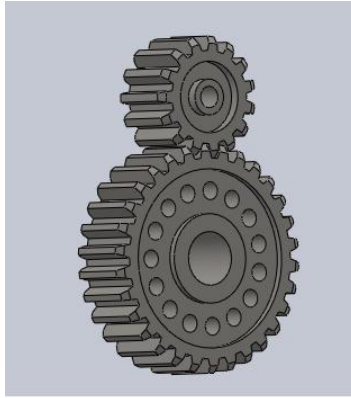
Sistema de engranajes para la transmisión de potencia del servomotor, el piñón se denomina al engrane pequeño.
